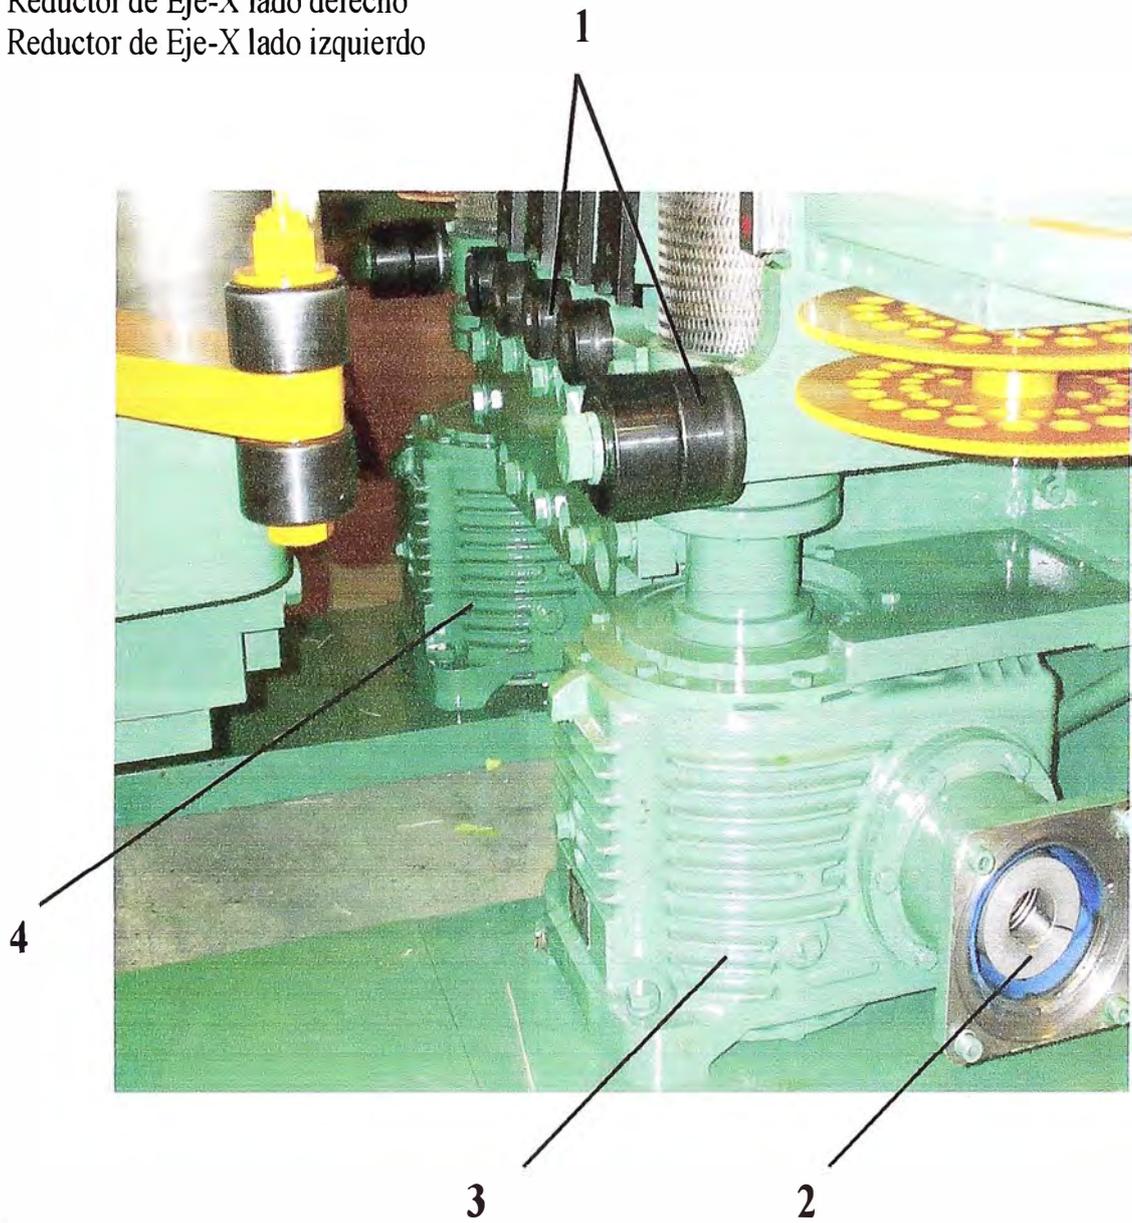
Unidad Taladradora - Equipo Mecánico
